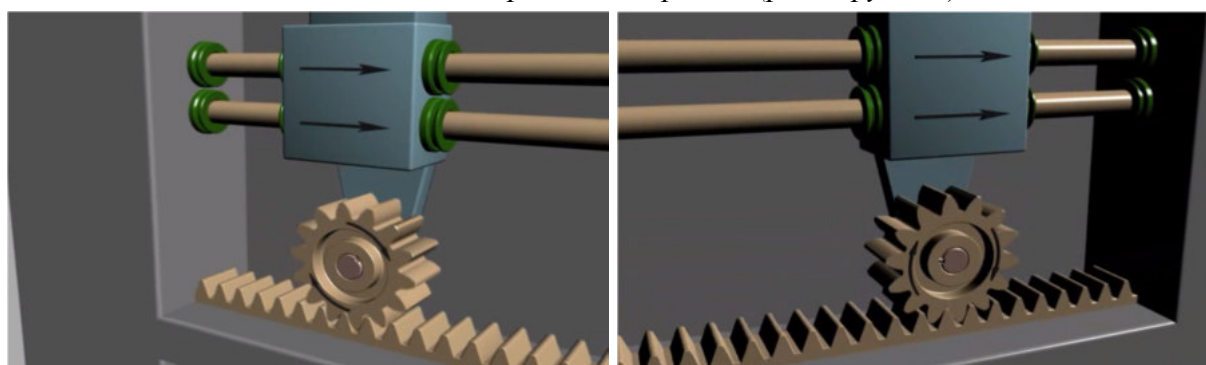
3D-модель рейкової передачі (рейка не рухома)
